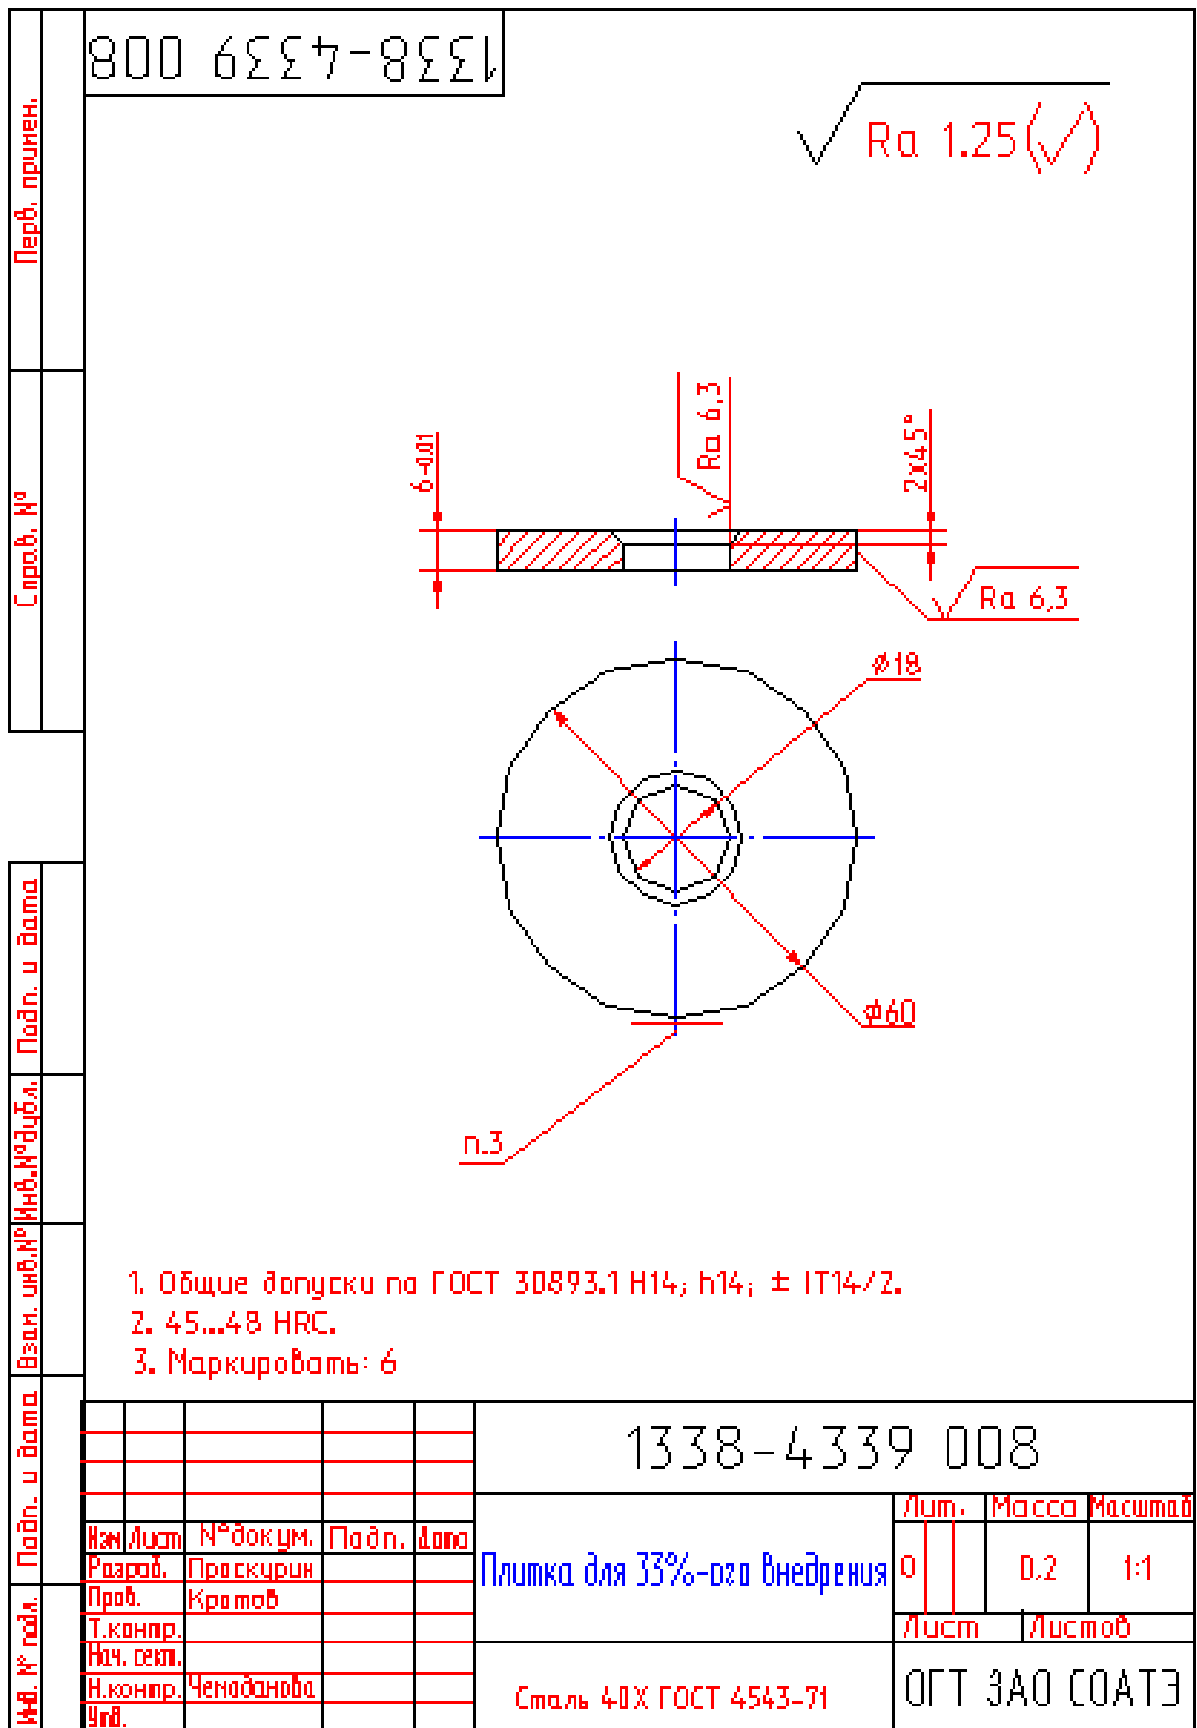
Деталь экспериментального устройства, тарированная Плитка, которая обеспечивает внедрение Пуансон-матрицы в заготовку на 33% от толщины заготовки
